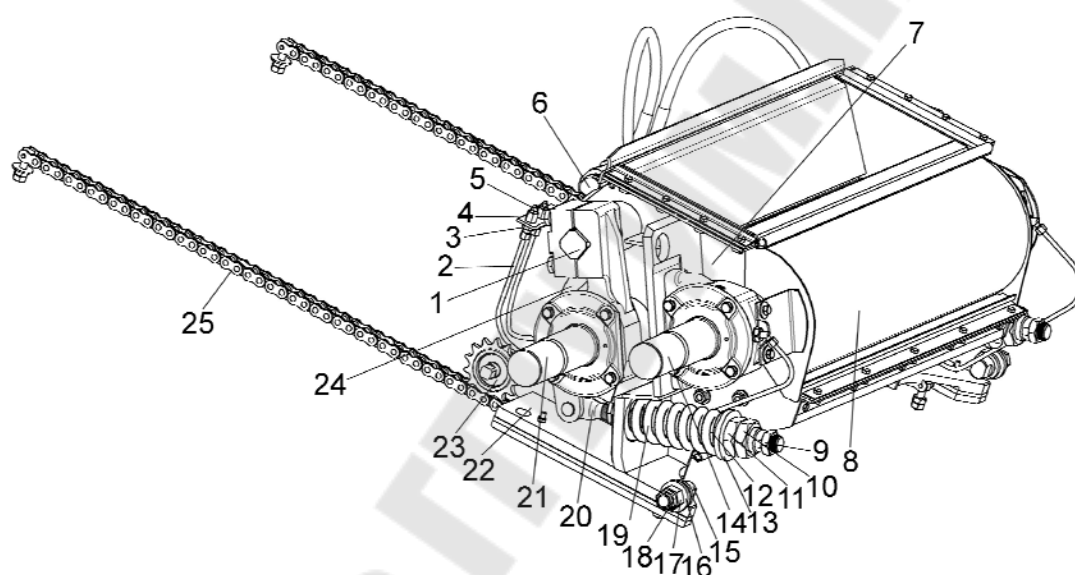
Устройство доизмельчающее: 1 – вал; 2 – трубка; 3, 11, 17 – гайки; 4 – штуцер; 5 – масленка; 6 – гидросистема регулировки зазора; 7 – корпус; 8 – кожух верхний; 9, 10, 18 – контргайки; 12 – гильза; 13, 16 – шайбы; 14 – валец верхний; 15 – упор; 19 – пружина; 20 – тяга; 21 – валец нижний; 22 – опора; 23 – механизм перемещения; 24 – кожух нижний; 25 – цепь
